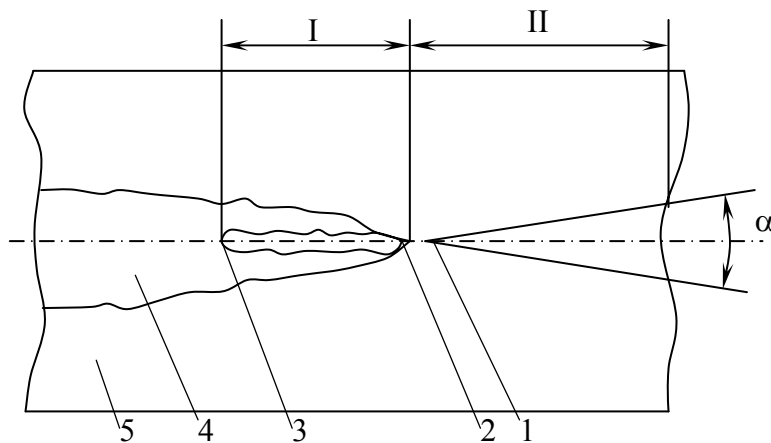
Схема участка высокочастотной сварки трубы: I – участок нагрева кромок трубной заготовки; II – участок оплавления; 1 – точка охлаждения; 2 – перемычка; 3 – точка соединения; 4 – грат; 5 – труба; α – угол схождения кромок трубной заготовки
